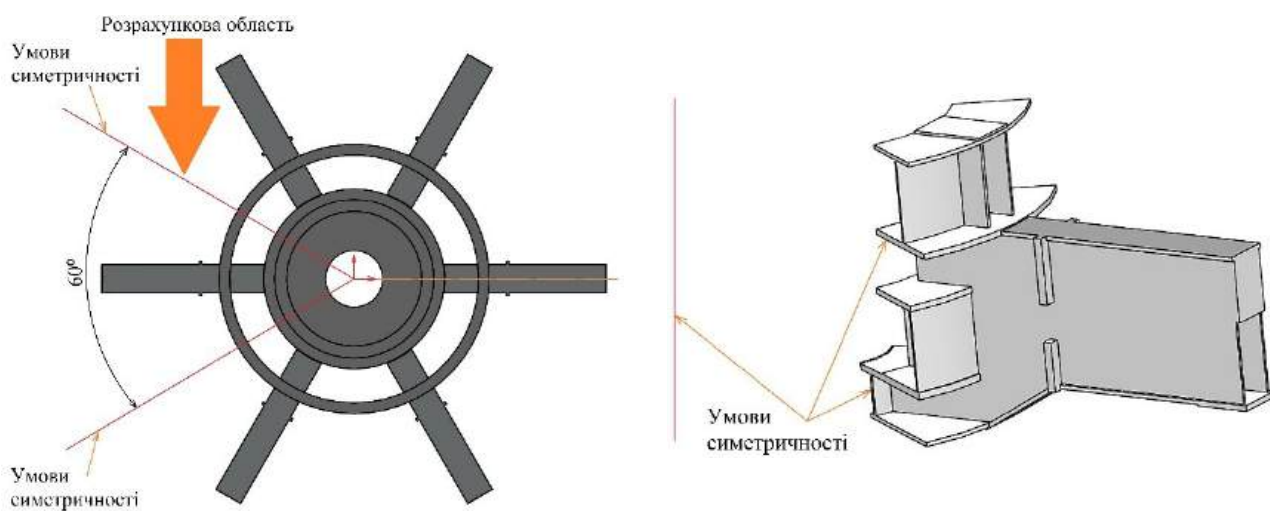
Розрахункова область модернізованої верхньої хрестовини
